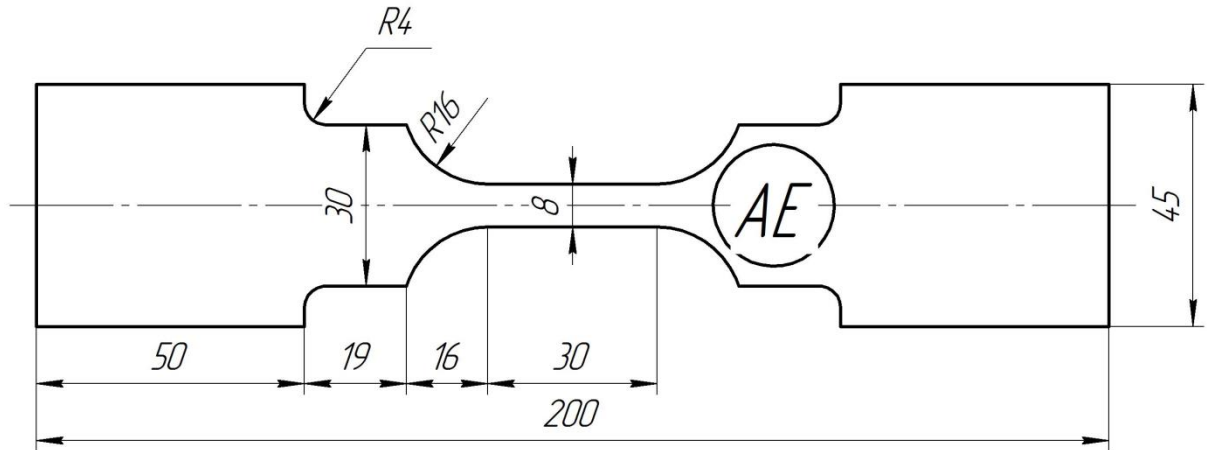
Чертеж образца ТРИП/ТВИП сталей для испытания на одноосное растяжение; место расположения датчика АЭ обозначено «АЭ»
